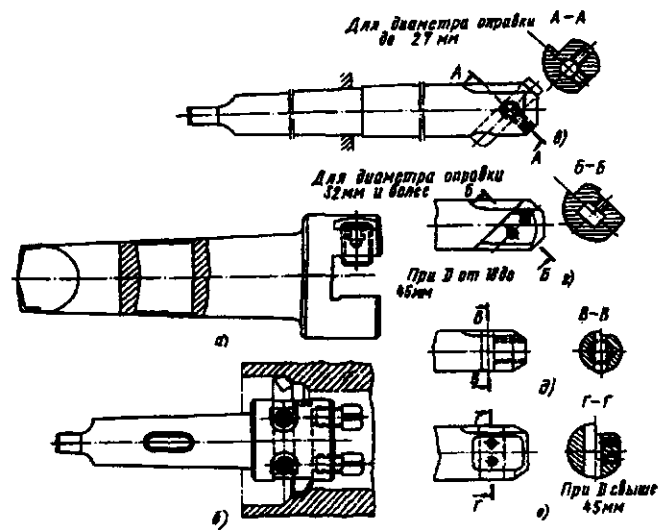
Консольные оправки для крепления режущих инструментов: а – короткая для одного реза; б – то же, для двух резов; в – удлиненная с наклонным креплением резов и круглым окном; г – то же, с прямоугольным окном; д – удлиненная с прямым креплением резов и квадратным окном; е – то же, с прямоугольным окном
